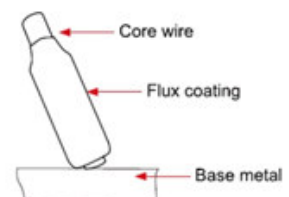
Grundlagen des MMA-Schweißens
